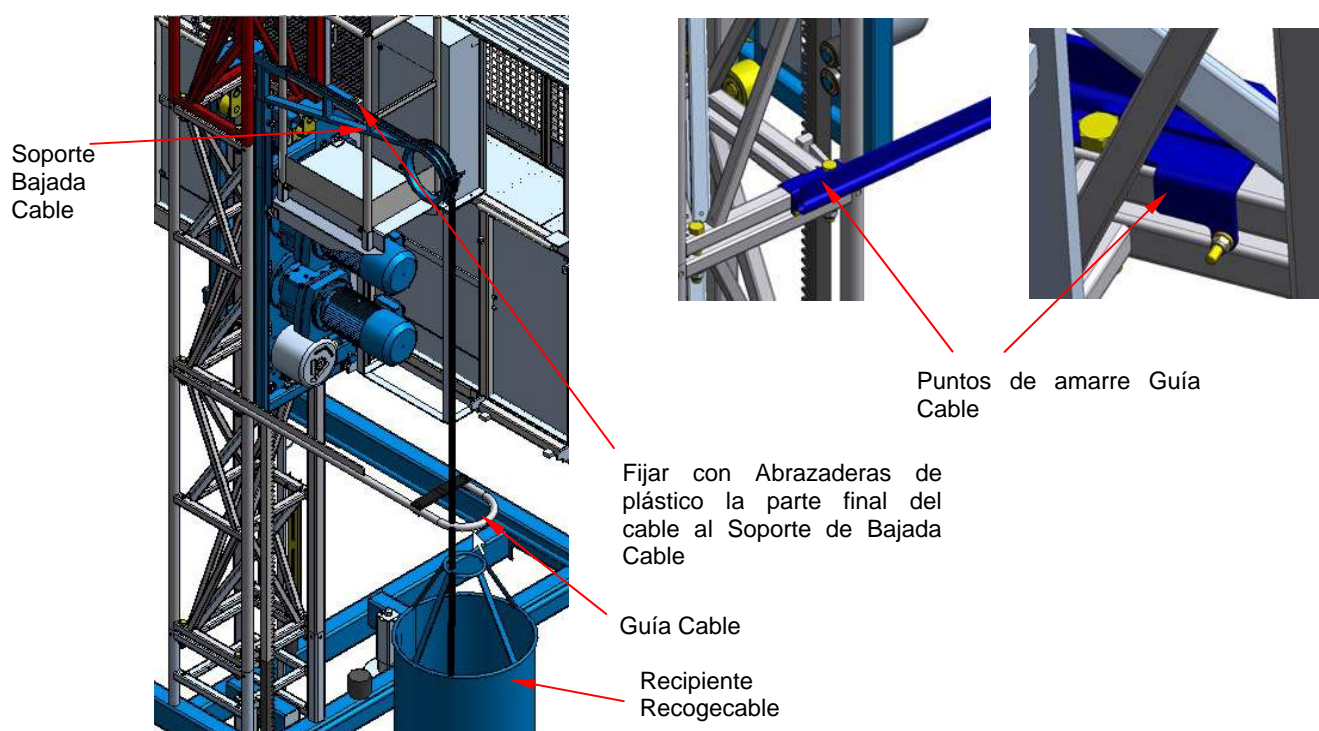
Guía Cable y Soporte Bajada Cable
